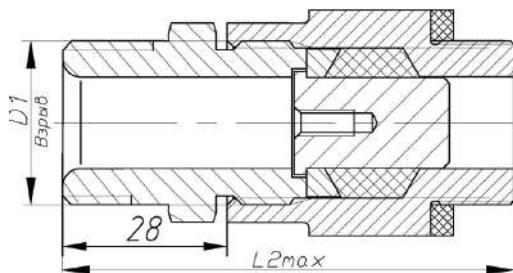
Конструкция кабельного ввода ExKV-T для прокладки кабеля в трубе. Остальное смотри рис.6.
